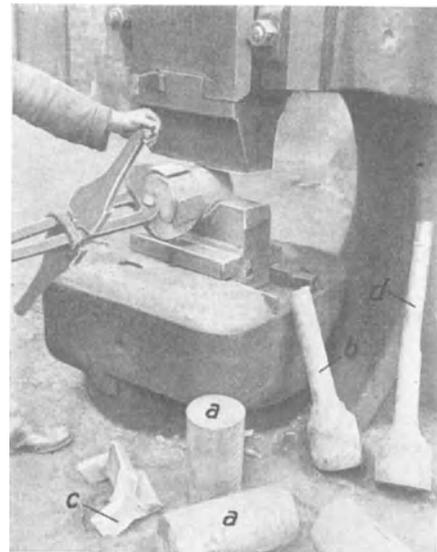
Strecken der Rohlinge unter dem Dampfhammer.
